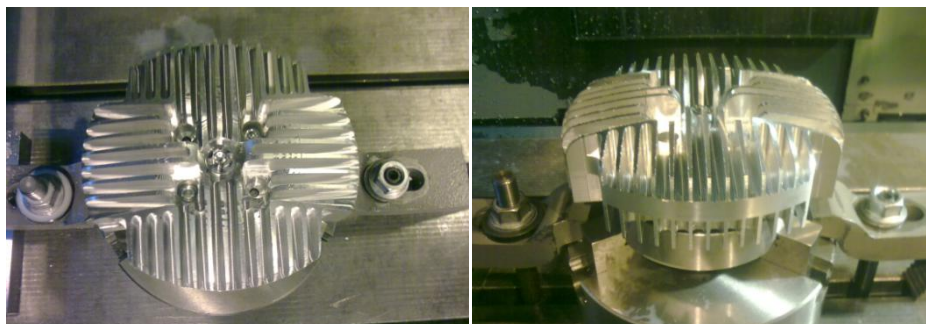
Obrobení bočního tvaru hlavy a průchozích děr pro šrouby
